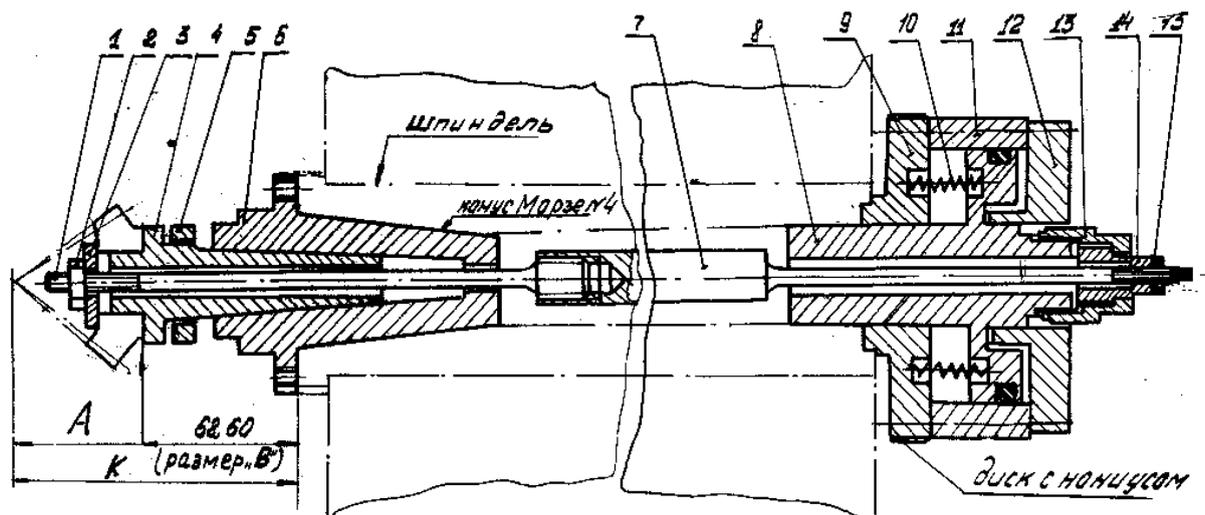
Механизм крепления нарезаемого зубчатого колеса:
